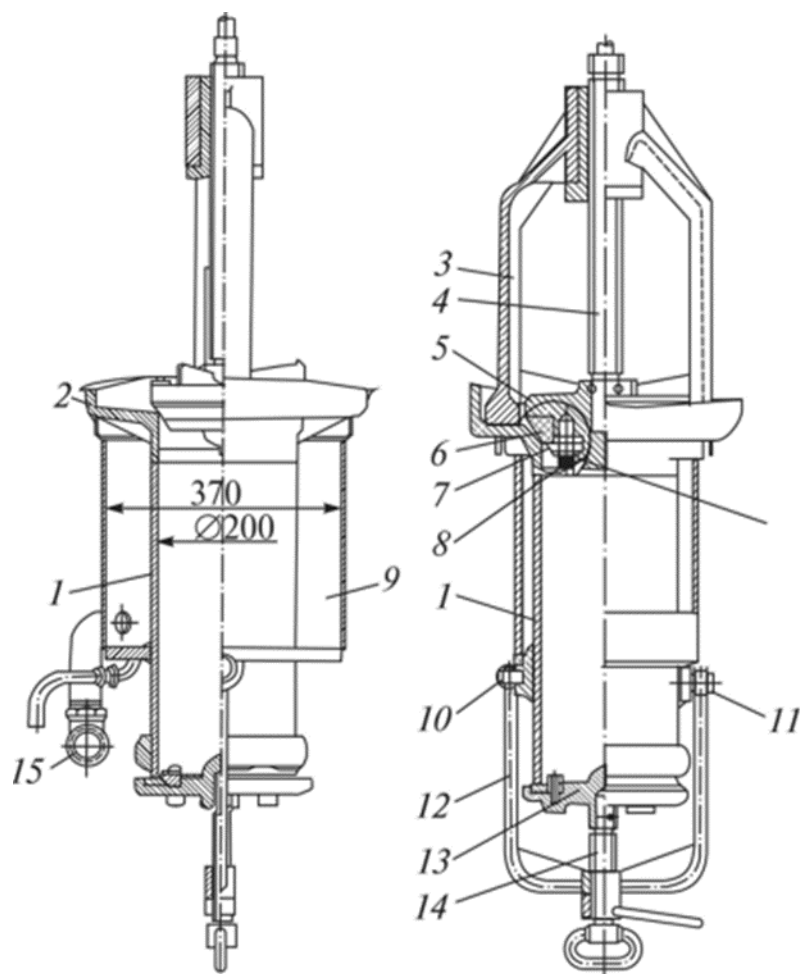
Універсальний зливний прилад сторої конструкції
